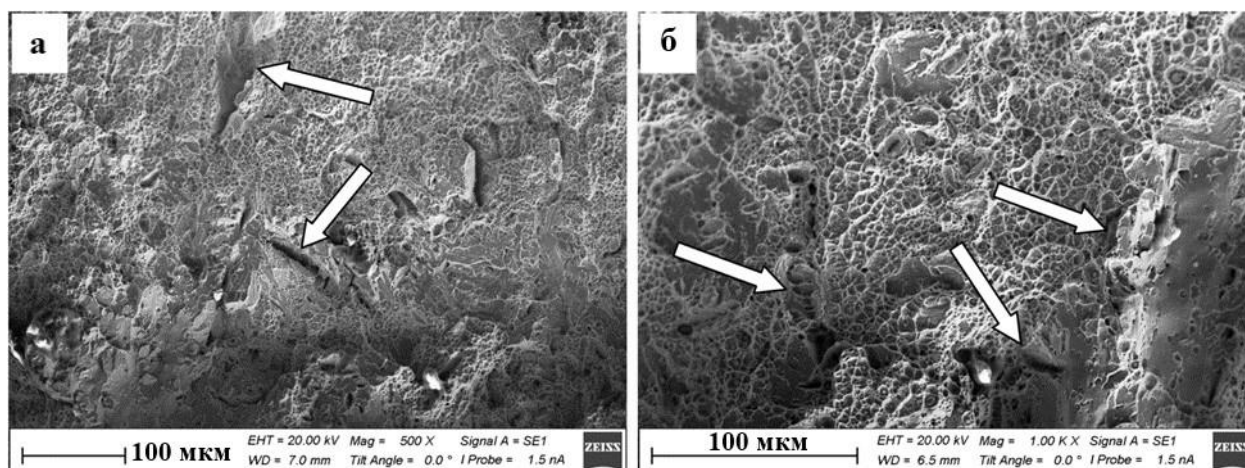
Структура поверхности излома металла наплавки (стрелками указаны области хрупкого излома, содержащие микротрещины)
